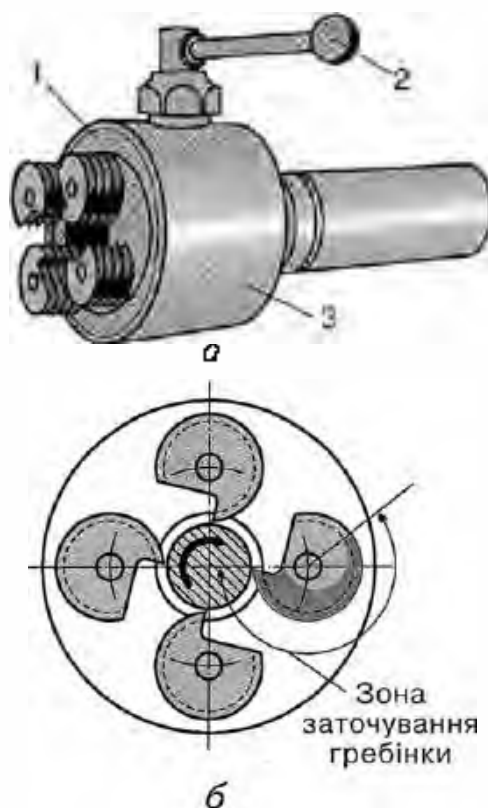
САМОРОЗКРИВНА ГОЛОВКА ДЛЯ НАРІЗУВАННЯ РІЗЬБИ
